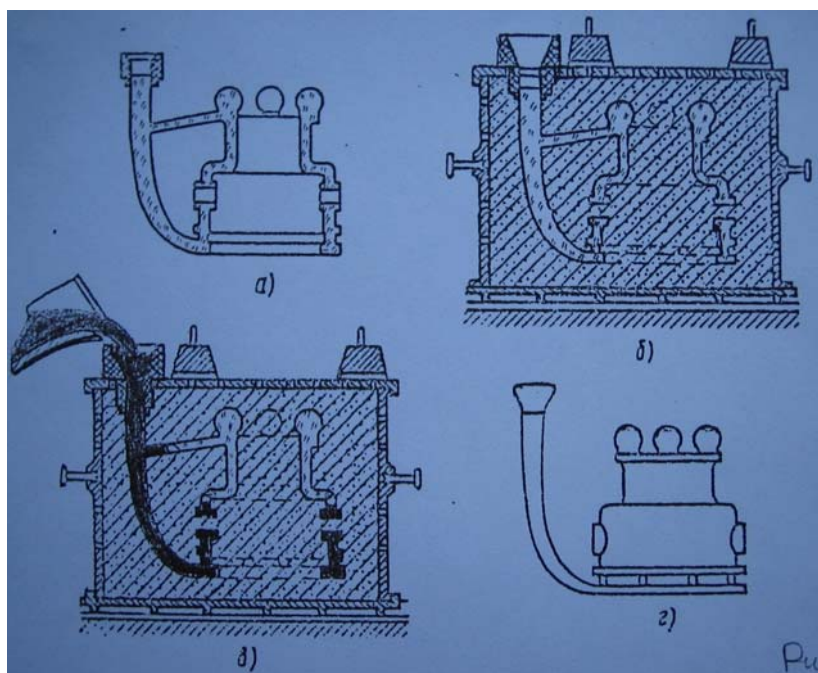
Схема изготовления отливки по газифицируемой модели.
